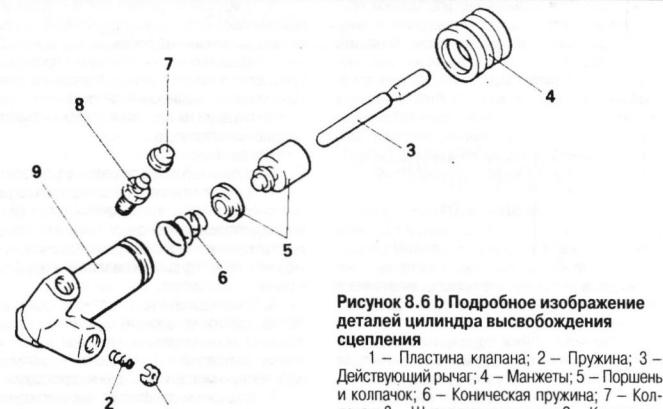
б Подробное изображение деталей цилиндра высвобождения сцепления
